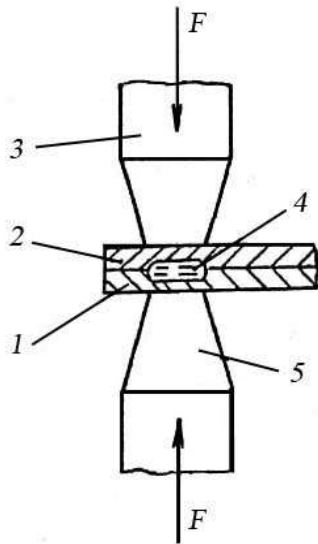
Схема точкового електроконтактного зварювання: 1, 2 - заготовка; 3, 5 - електрод; 4 - зварна точка; F - зовнішня сила
